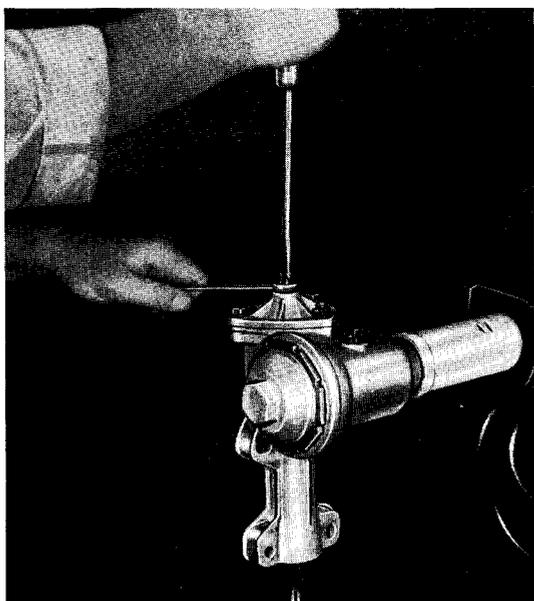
Einstellschraube aus Lenkgehäusedeckel bis zum Anschlag herausschrauben
